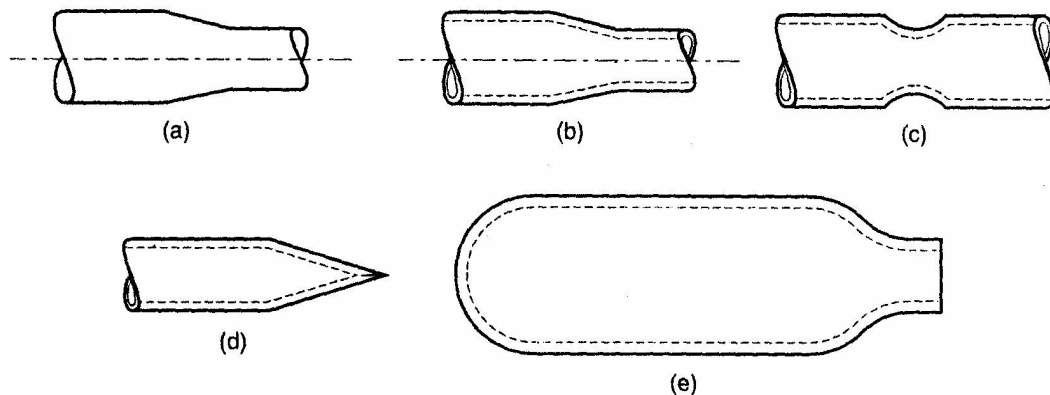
Ejemplos de partes hechas por estampado (a) reducción de material sólido, (b) ahusado (le un tubo, (c) estampado para formar un canal en un tubo, (d) afilado de un tubo y (e) estampado del cuello en un cilindro de gas.
